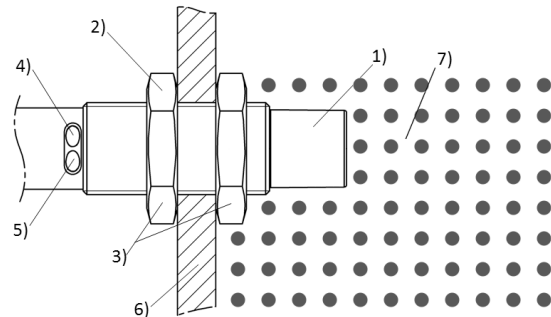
Abgleich mit Schüttgut, 1) Aktive Fläche, 2) Befestigungsgewinde M12x1, 3) Befestigungsmuttern, 4) Anzeige Sensorzustand (grüne LED), 5) Anzeige Schaltzustand (gelbe LED), 6) Behälterwand, 7) Schüttgut
